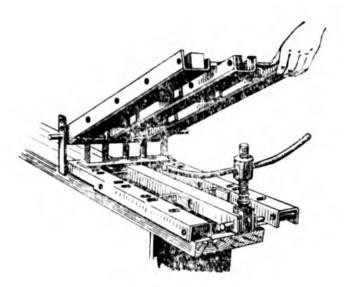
Пресс-форма для изготовления тростниковых шалашиков
